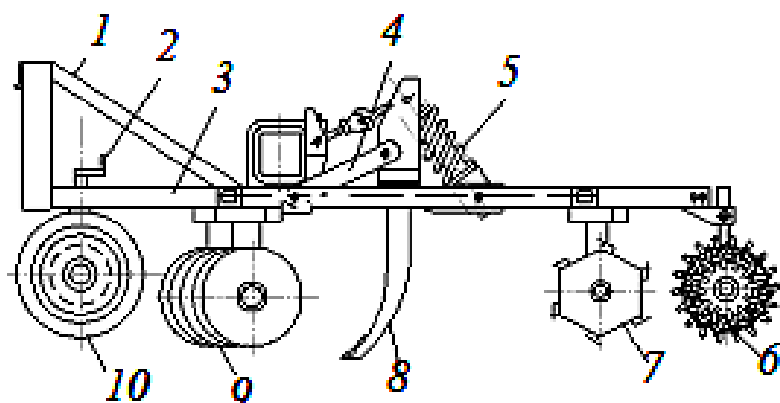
Комбінований агрегат для протиерозійної обробки ґрунту: 1 – навіска; 2 – регулювальний гвинт; 3 – несуча система; 4 – паралелограмний механізм; 5 – пружина; 6 – барабан-вирівнювач; 7 – штангово-зубчастий каток; 8 – плоскорізальні вузькозахватні лапи; 9 – дискові батареї; 10 – опорні колеса.
